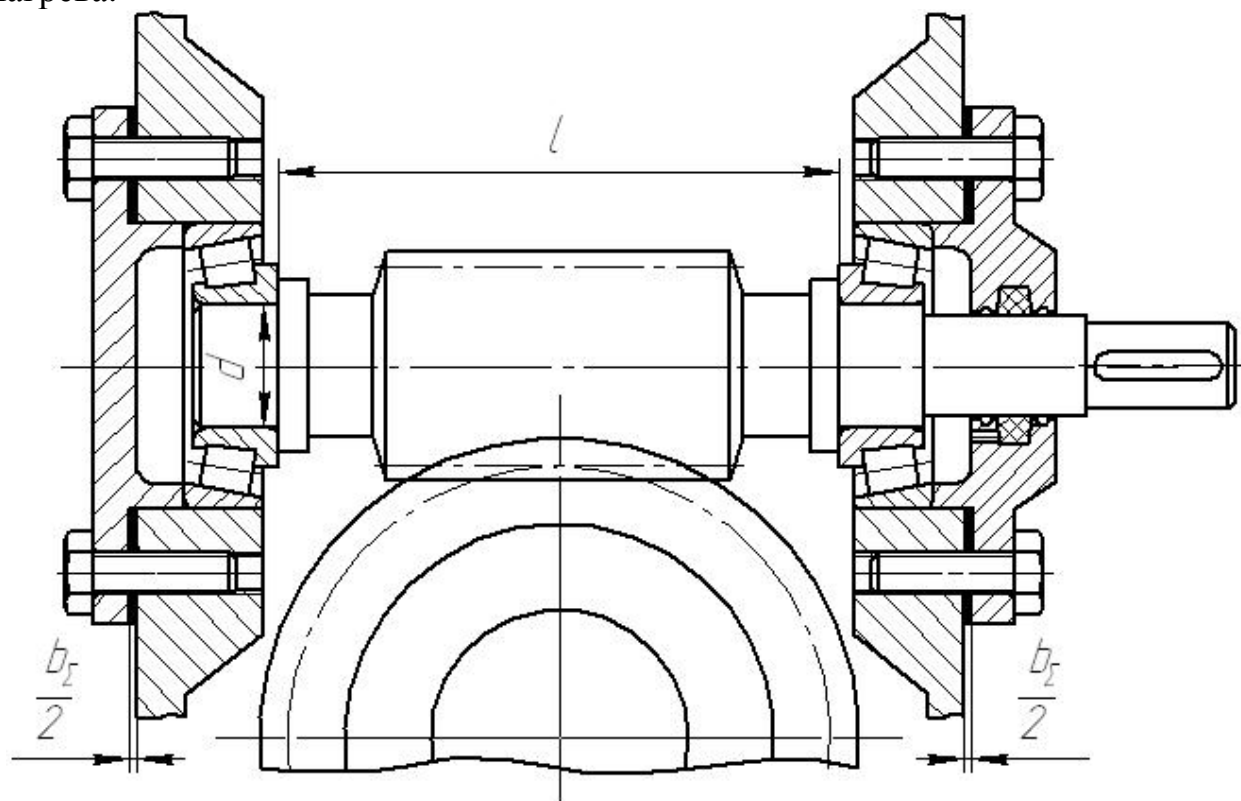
Узел вала червяка с подшипниками, установленными «враспор»
